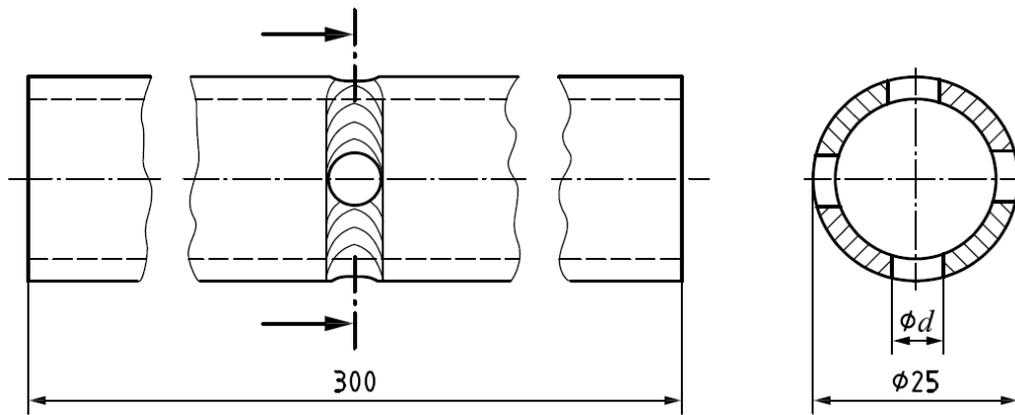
管对接焊缝断裂及弯曲试验取样位置检验长度
